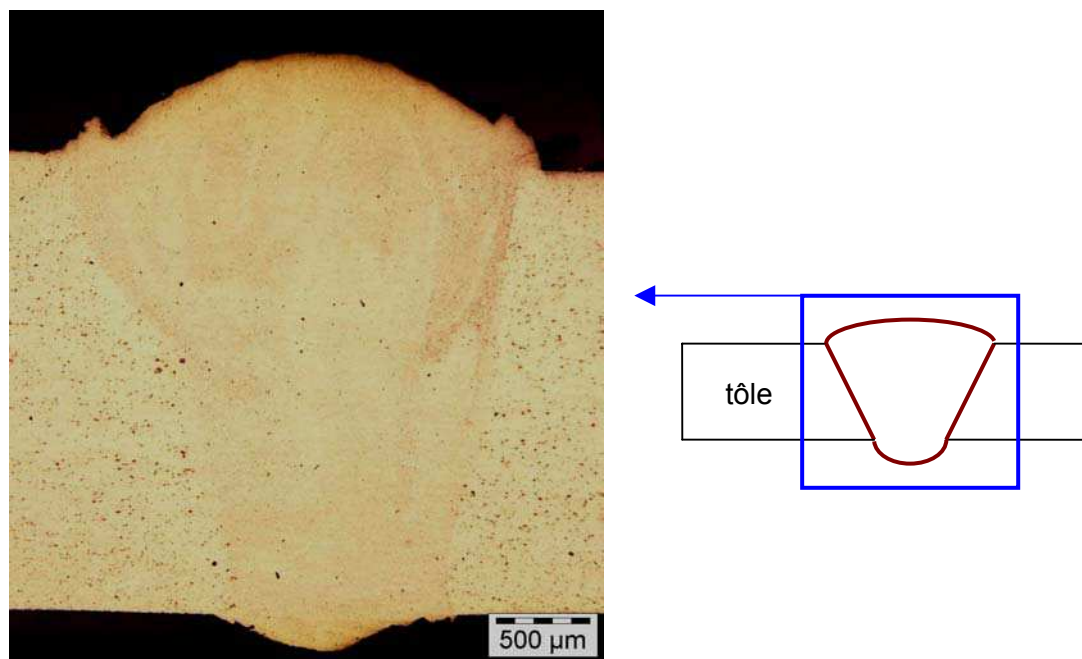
Vue générale d'un soudure bord à bord
